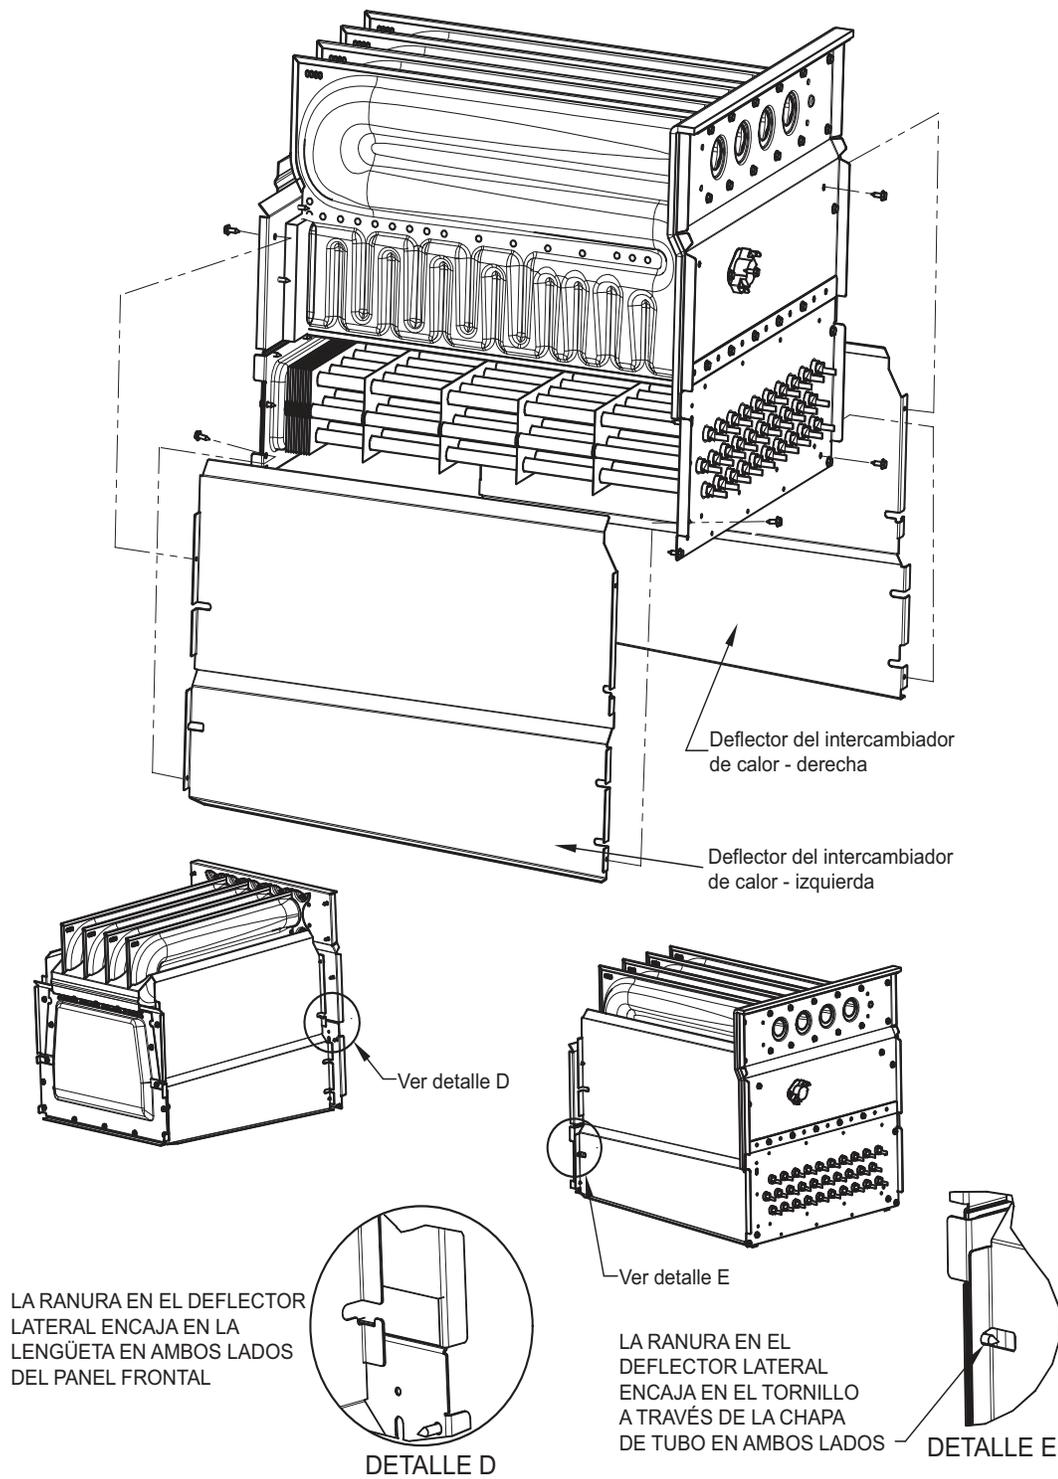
Ensamblaje del panel del intercambiador de calor
